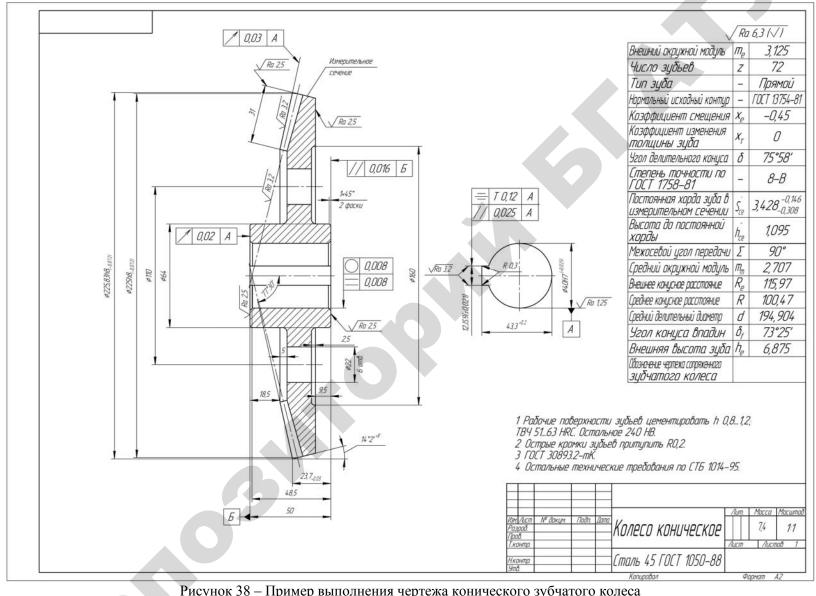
Пример выполнения чертежа конического зубчатого колеса
